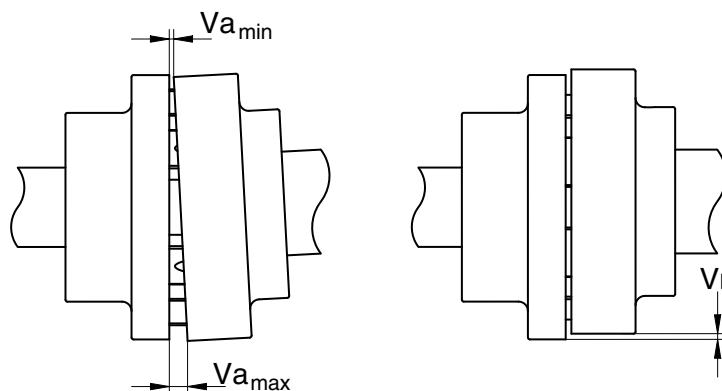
Стандартная муфта с допусками при совмещении
